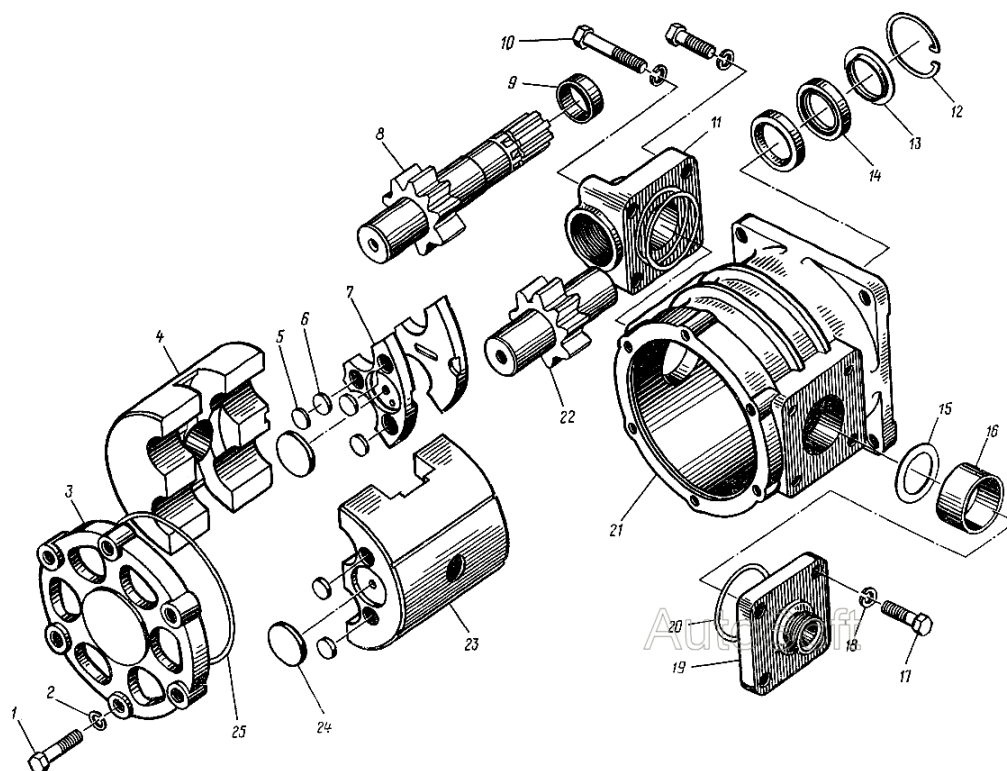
Насос гидравлический НШ-100 ЛЗА 4014: 1 - Болт М12х50, 2 – Шайба, 3 – Крышка, 4 - Обойма подшипника, 5 - Пластина, 6 – Манжета, 7 - Платик, 8 - Шестерня ведущая, 9 – Втулка, 10 - Болт М12х75, 11 - Муфта угловая, 12 - Кольцо стопорное, 13 - Кольцо опорное, 14 – Манжета, 15 - Пластина опорная, 16 – Манжета, 17 - Болт М12х40, 19 – Фланец, 20 - Кольцо уплотнительное, 21 – Корпус, 22 - Шестерня ведомая, 23 - Обойма поджимная, 24 – Манжета, 25 - Кольцо уплотнительное.
